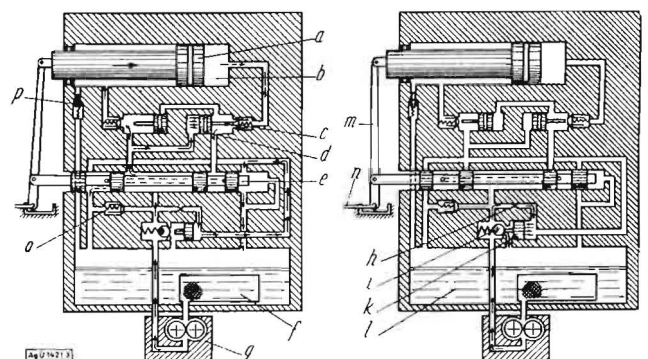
Kraftzylinder mit zweiseitiger Wirkung
